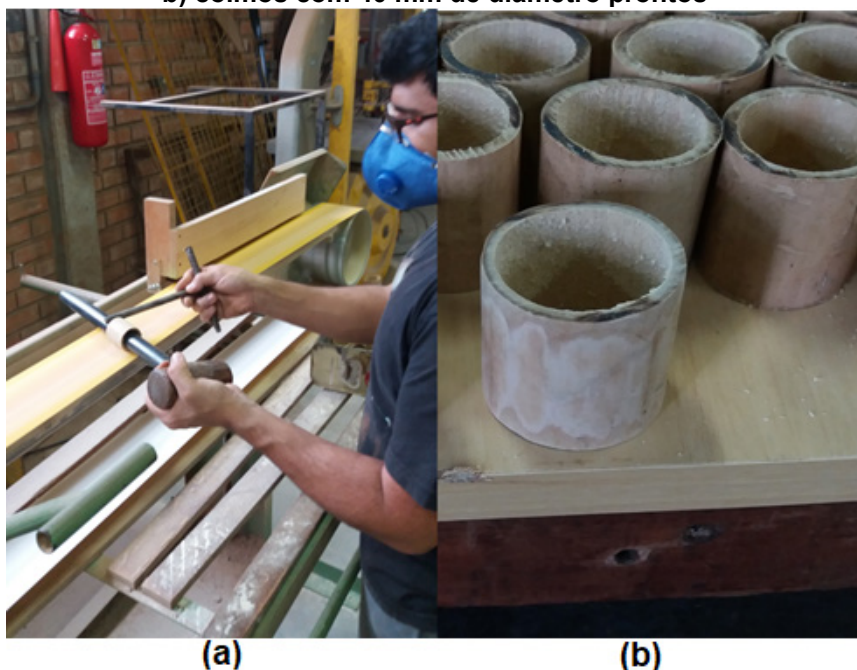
Corte e preparação do bambu: a) corte do bambu com 40 mm de diâmetro b) preparação para armazenamento
